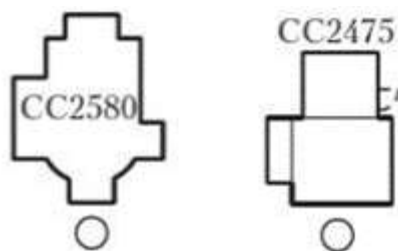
Свердлильні верстати (без вказання типу)
